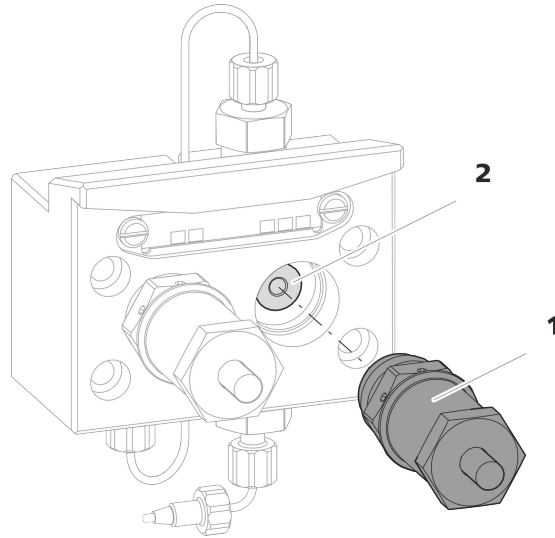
Desmontaje de cabezal de bomba – cartucho de pistón
